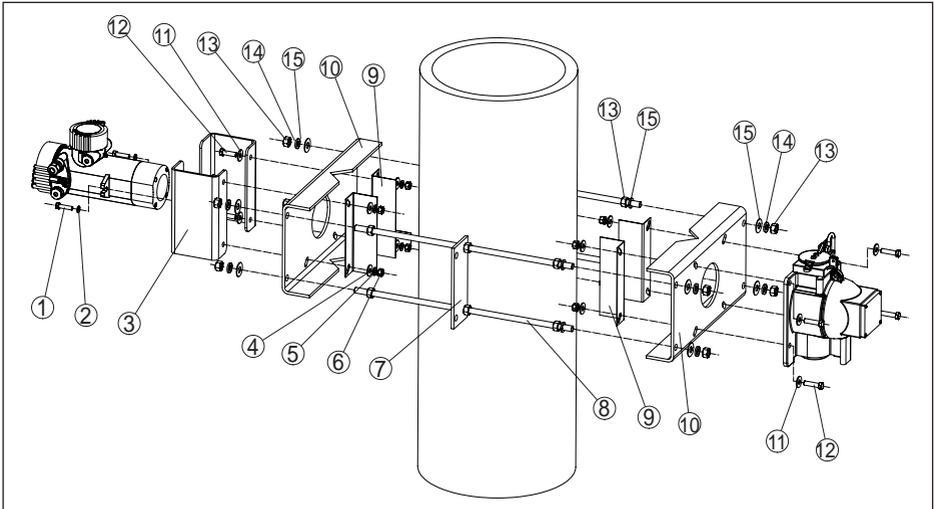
Dispositivo de sujeción con sensor montado horizontalmente
